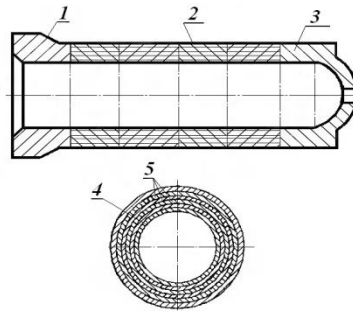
Багатошаровий корпус апарата високого тиску:
